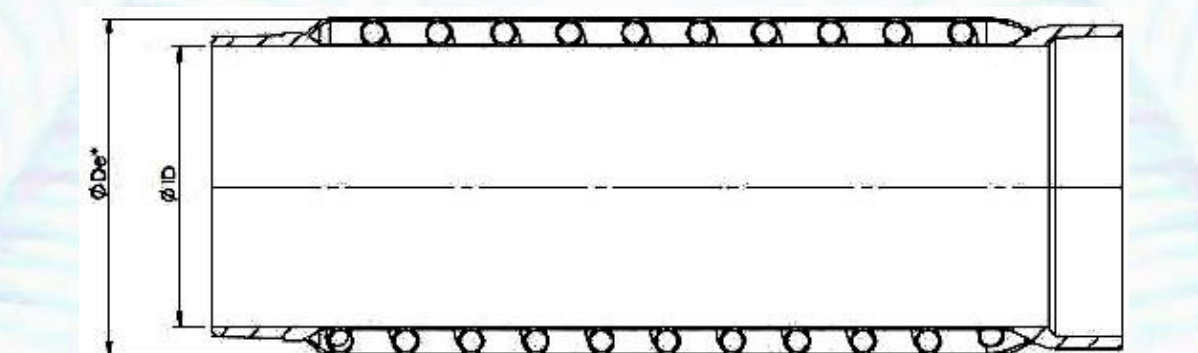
Общий вид и разрез трубы с профилем стенки «SPR»
